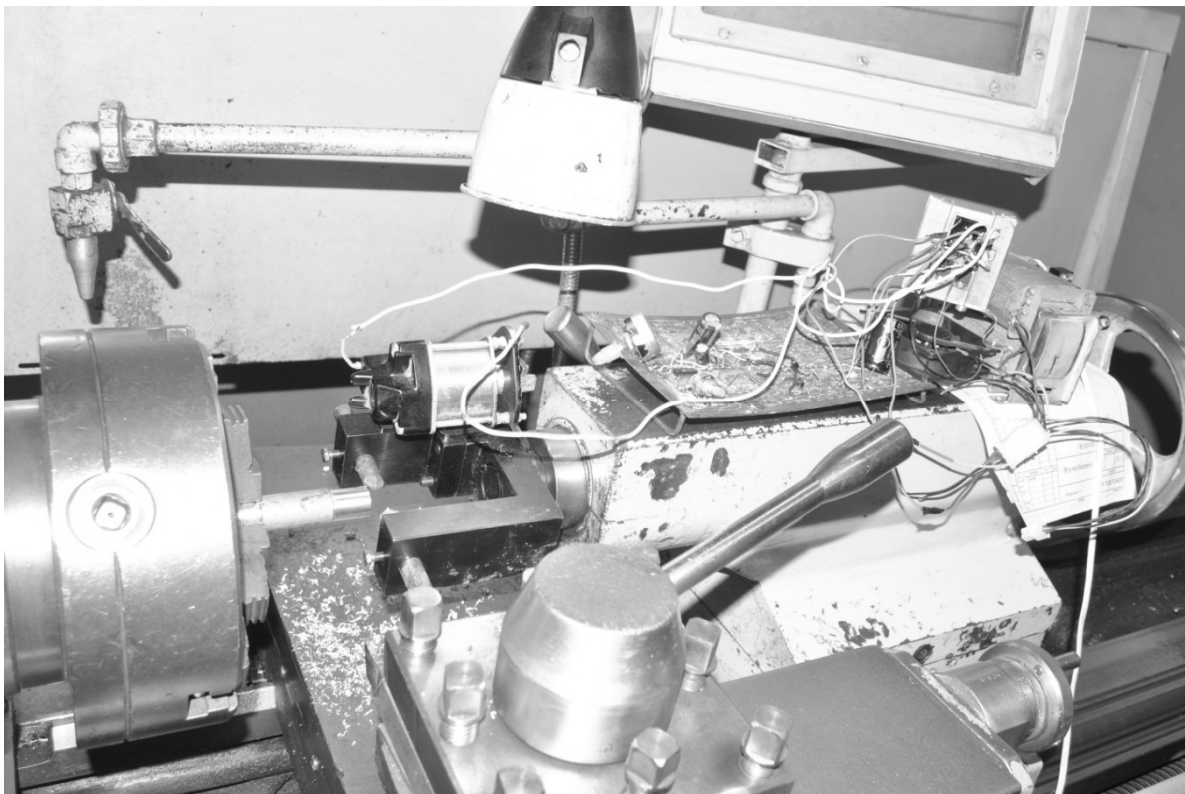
Фото установки для подрібнення стружки з електромеханічним зв'язком, встановленої на токарно-гвинторізному верстаті 16К30
